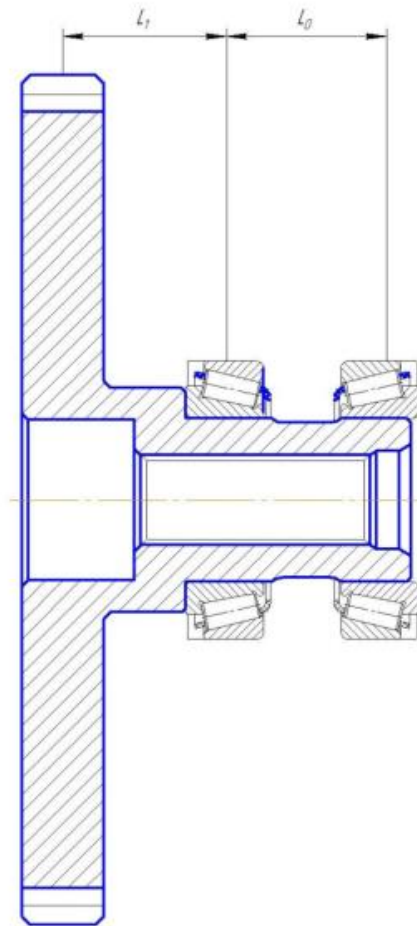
Конструкция ведущего вала переднего редуктора
